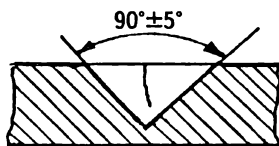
Разделка кромок под сварку при помощи трещины
